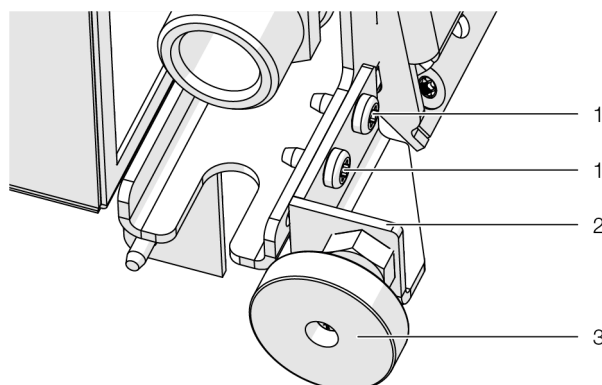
Befestigung des Montagefußes (hier obere Position)
